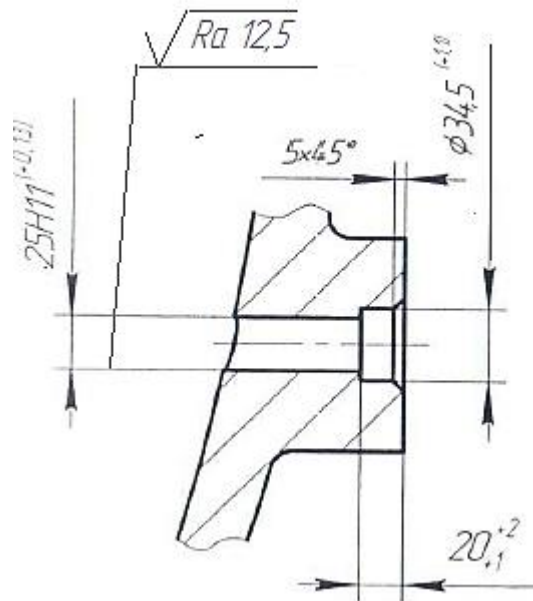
Эскиз обрабатываемого отверстия детали крышка.
